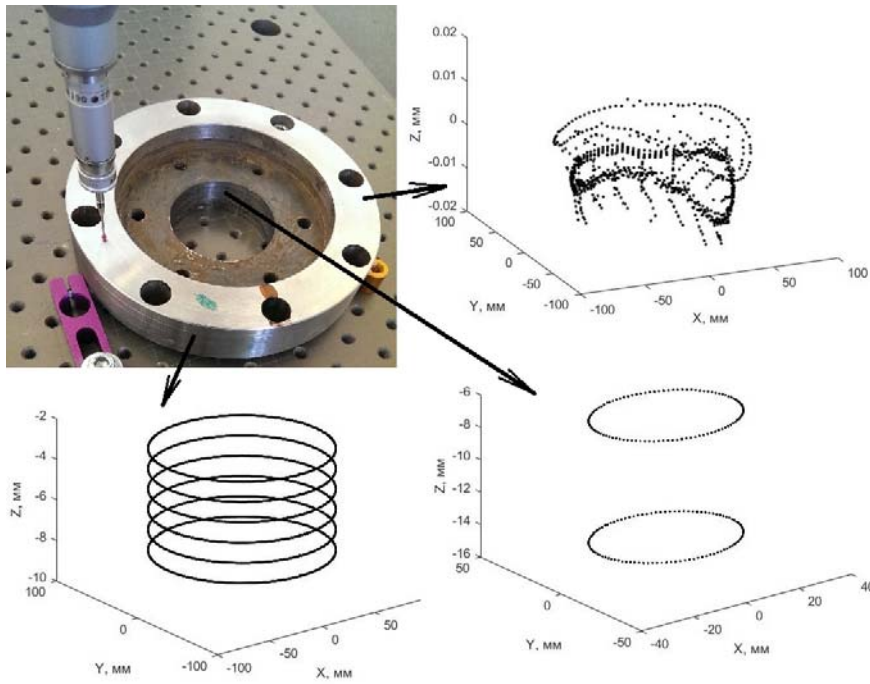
Деталь-имитатор диска и измеренные точки его поверхностей
